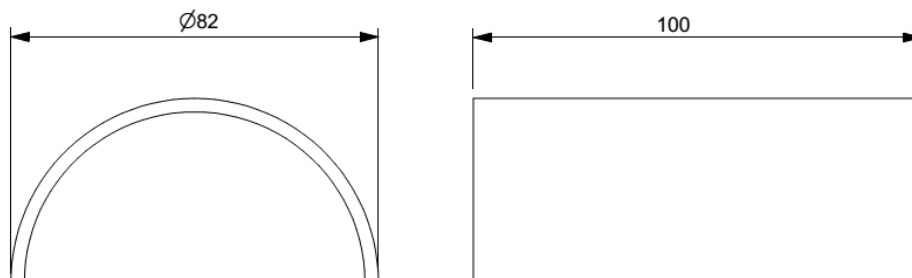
Representação dos provetes com diâmetro exterior de 82 mm e 100 mm de comprimento. Vista frontal e alçado lateral esquerdo.
